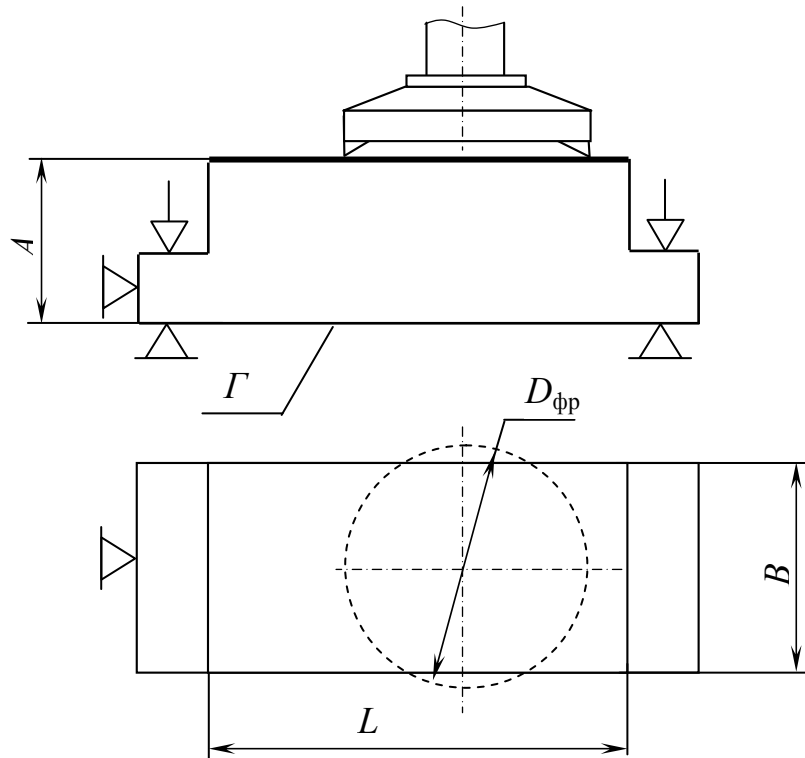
Операційний ескіз до визначення сумарної похибки фрезерної обробки
